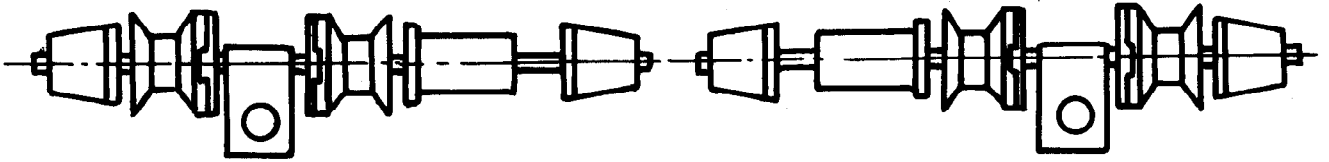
Type 4 — Guindeau à deux barbotins et à tambour à câble
